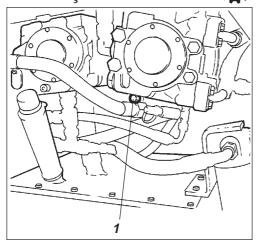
Engrenagem da bomba 1. Bujão de esvaziamento
